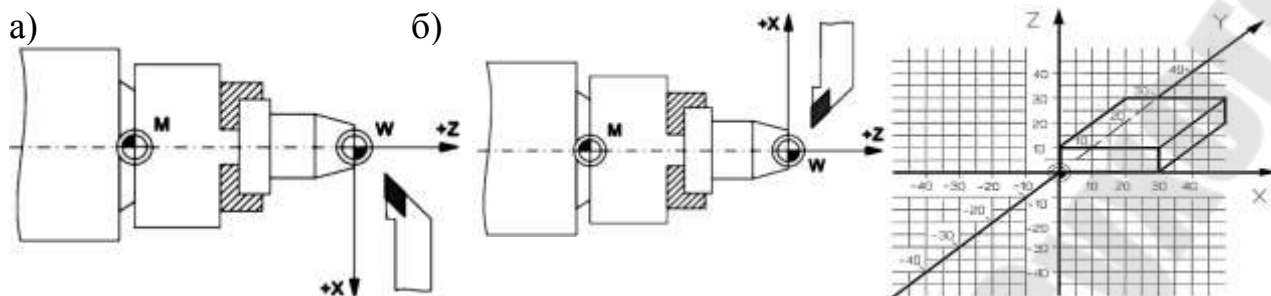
Расположение нулевой точки заготовки при обработке на токарном (а, б) и фрезерном (в) станках с ЧПУ
